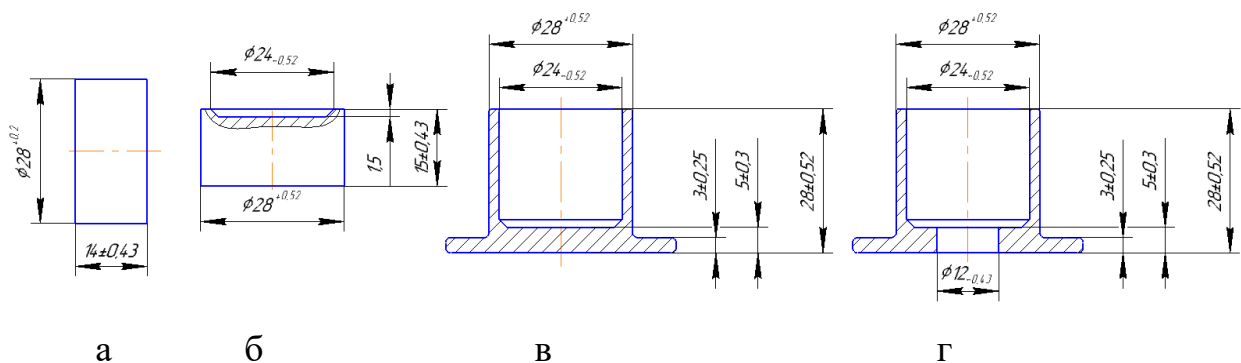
Ескізи технологічних переходів при штампування деталі типу стакан з фланцем: заготовка (а), калібрування (б) радіально-зворотне видавлювання (в) та пробивка отвору (г)
